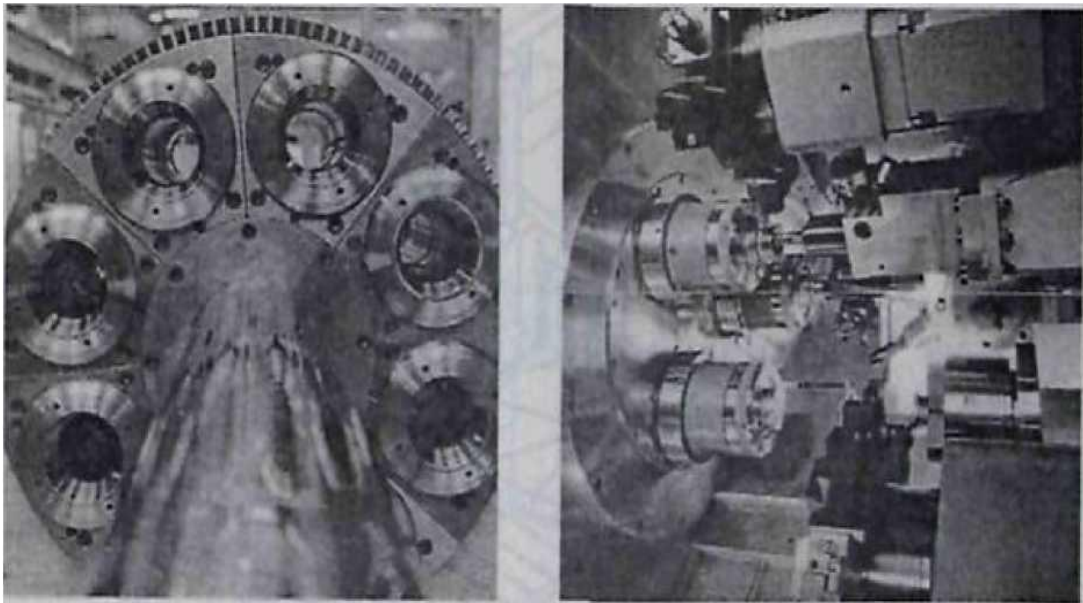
Револьверні головки з інструментами, що обертаються (а) і, які є нерухомими (б)
